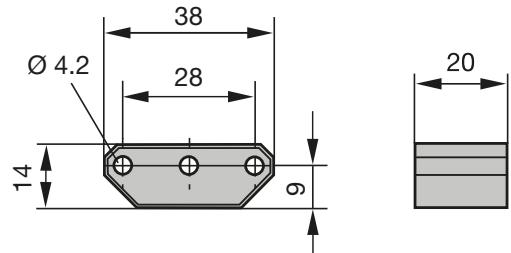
Dimensioni di ingombro datore di posizione BTL5-P-3800-2
